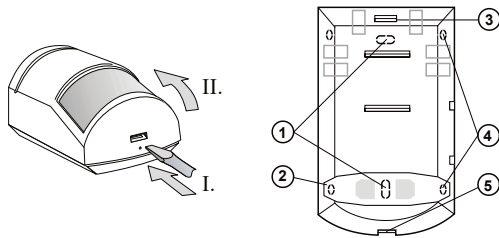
отверстия для установки на стене; 2, 4 – отверстия для установки в углу; 3 – защелка PCB; 5 – защелка крышки
